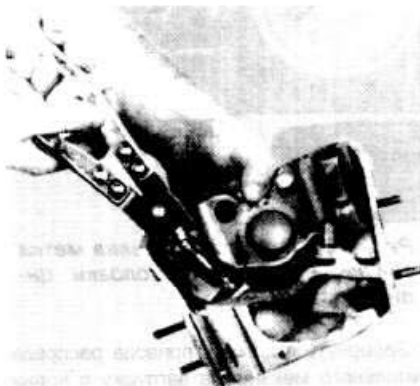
Снятие маслоотражательных колпачков клапанов с помощью приспособления BMW 11.1.480
